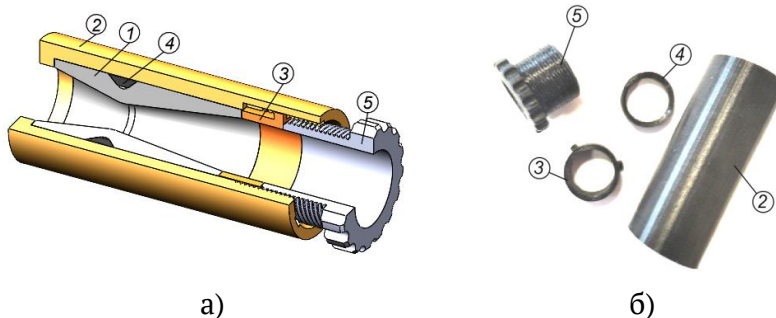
Пресформа для виготовлення еластичного сопла
